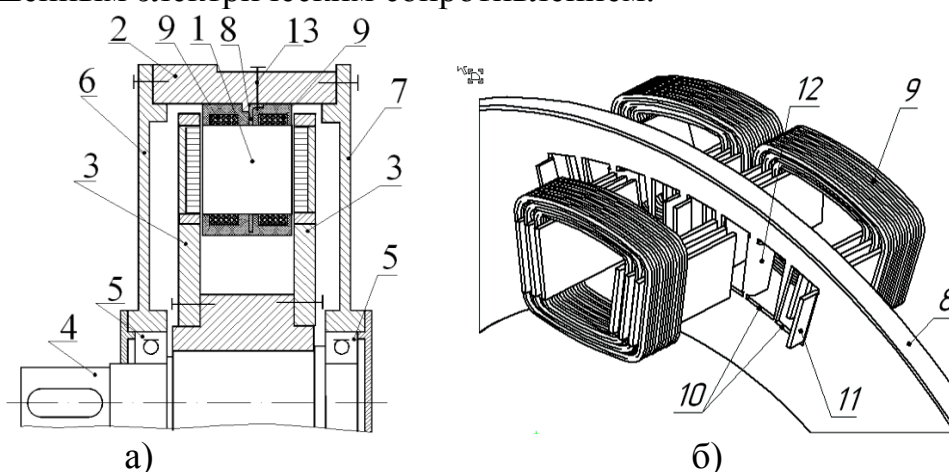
Торцевой асинхронный двигатель с АРС
